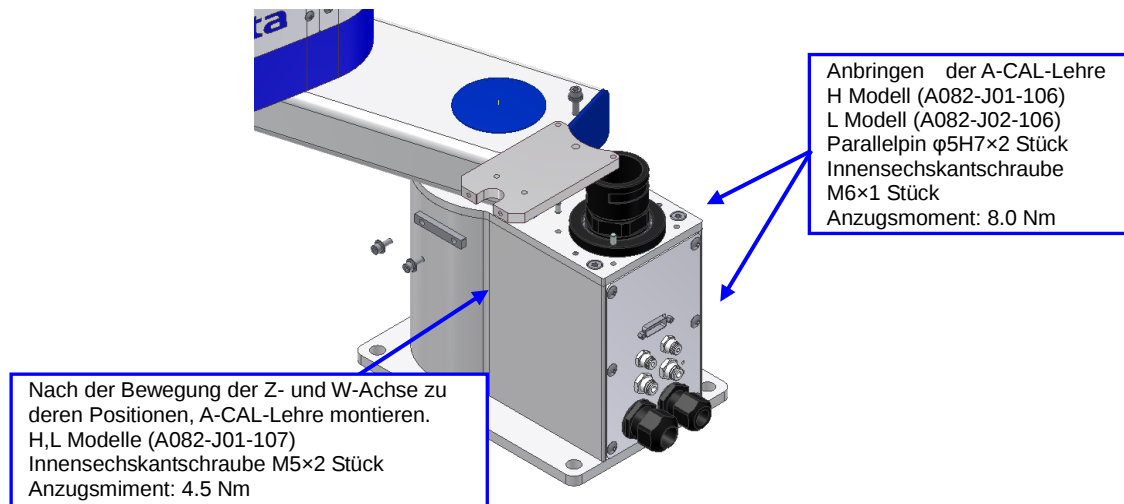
Detailzeichnung zum Anbringen der A-CAL-Lehre
